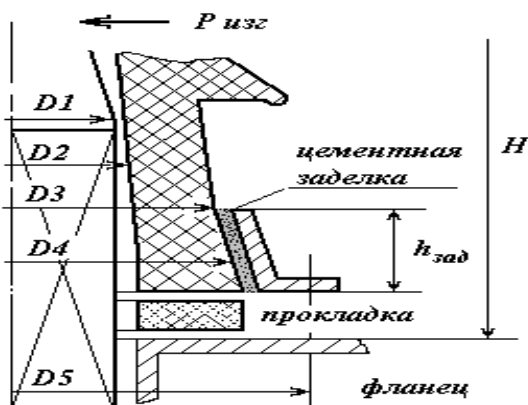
Крепление фарфоровой покрышки к фланцу с помощью цементной заделки (узел 2)
